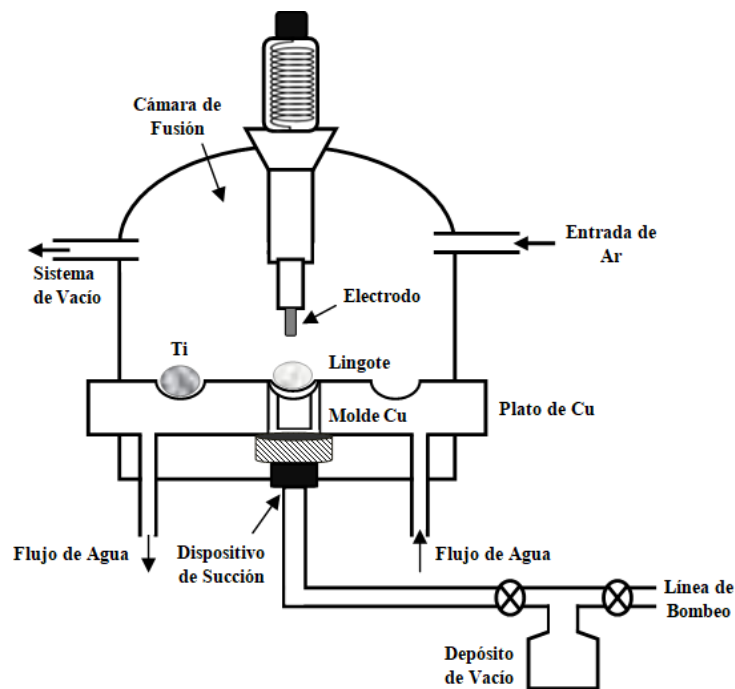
Esquema detallado de los componentes para llevar a cabo *suction casting
